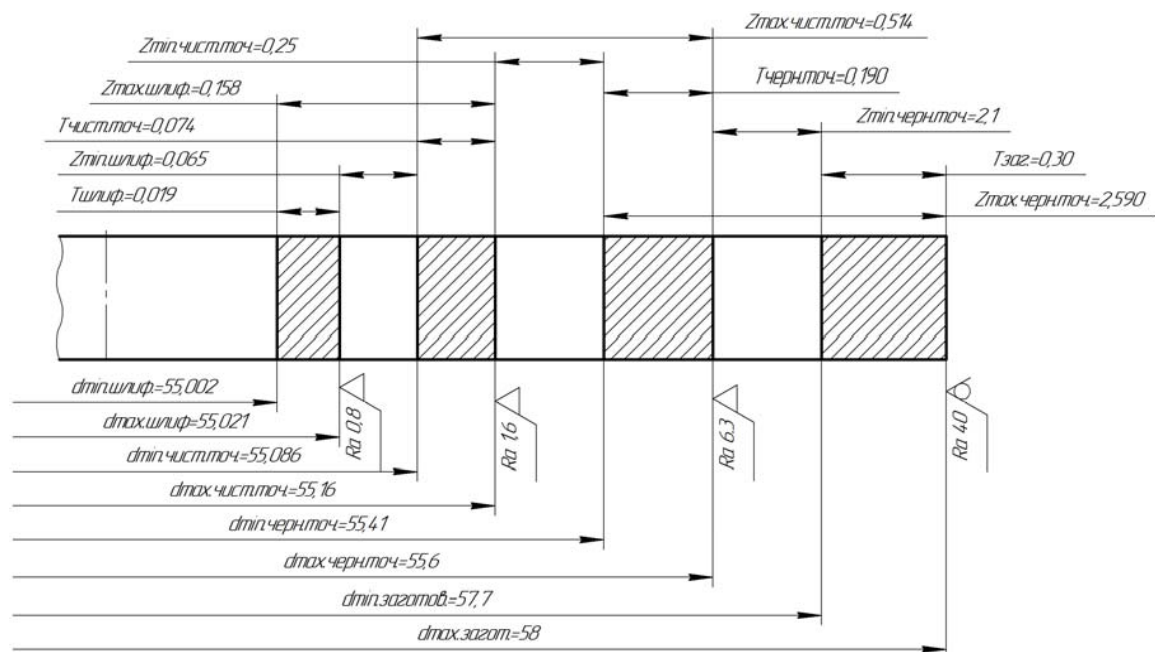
Схема розташування полів допусків та припусків на розмір  $\varnothing 55k6$ .
